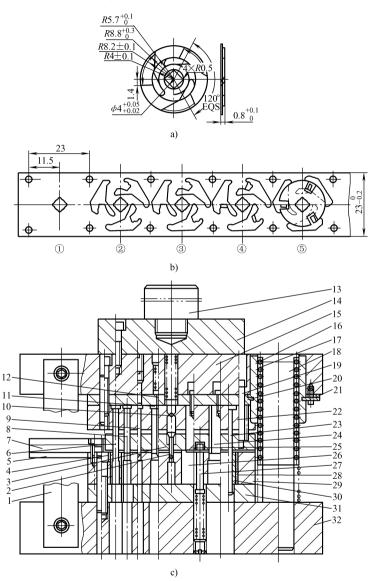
钟表元件二轮压簧级进模 a) 零件图 b) 排样图 c) 模具结构图
